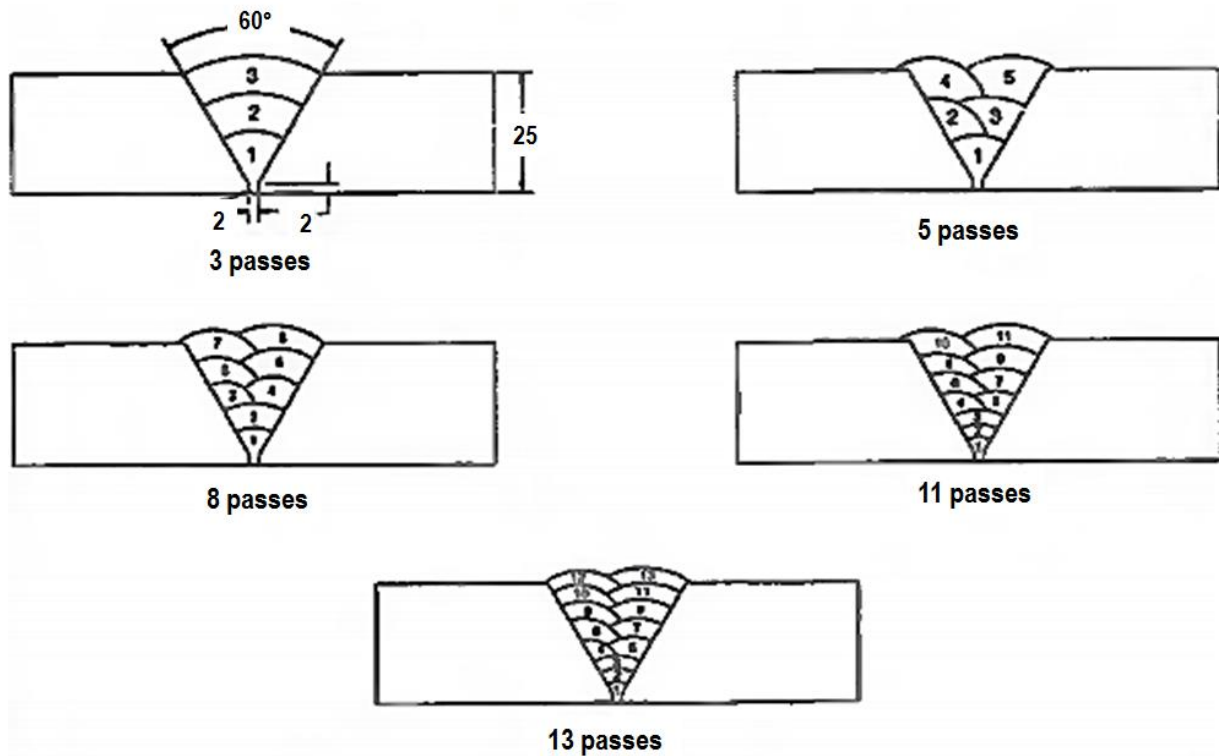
Seqüência de soldagem e detalhamento do chanfro (MURUGAN, et al., 2005).
